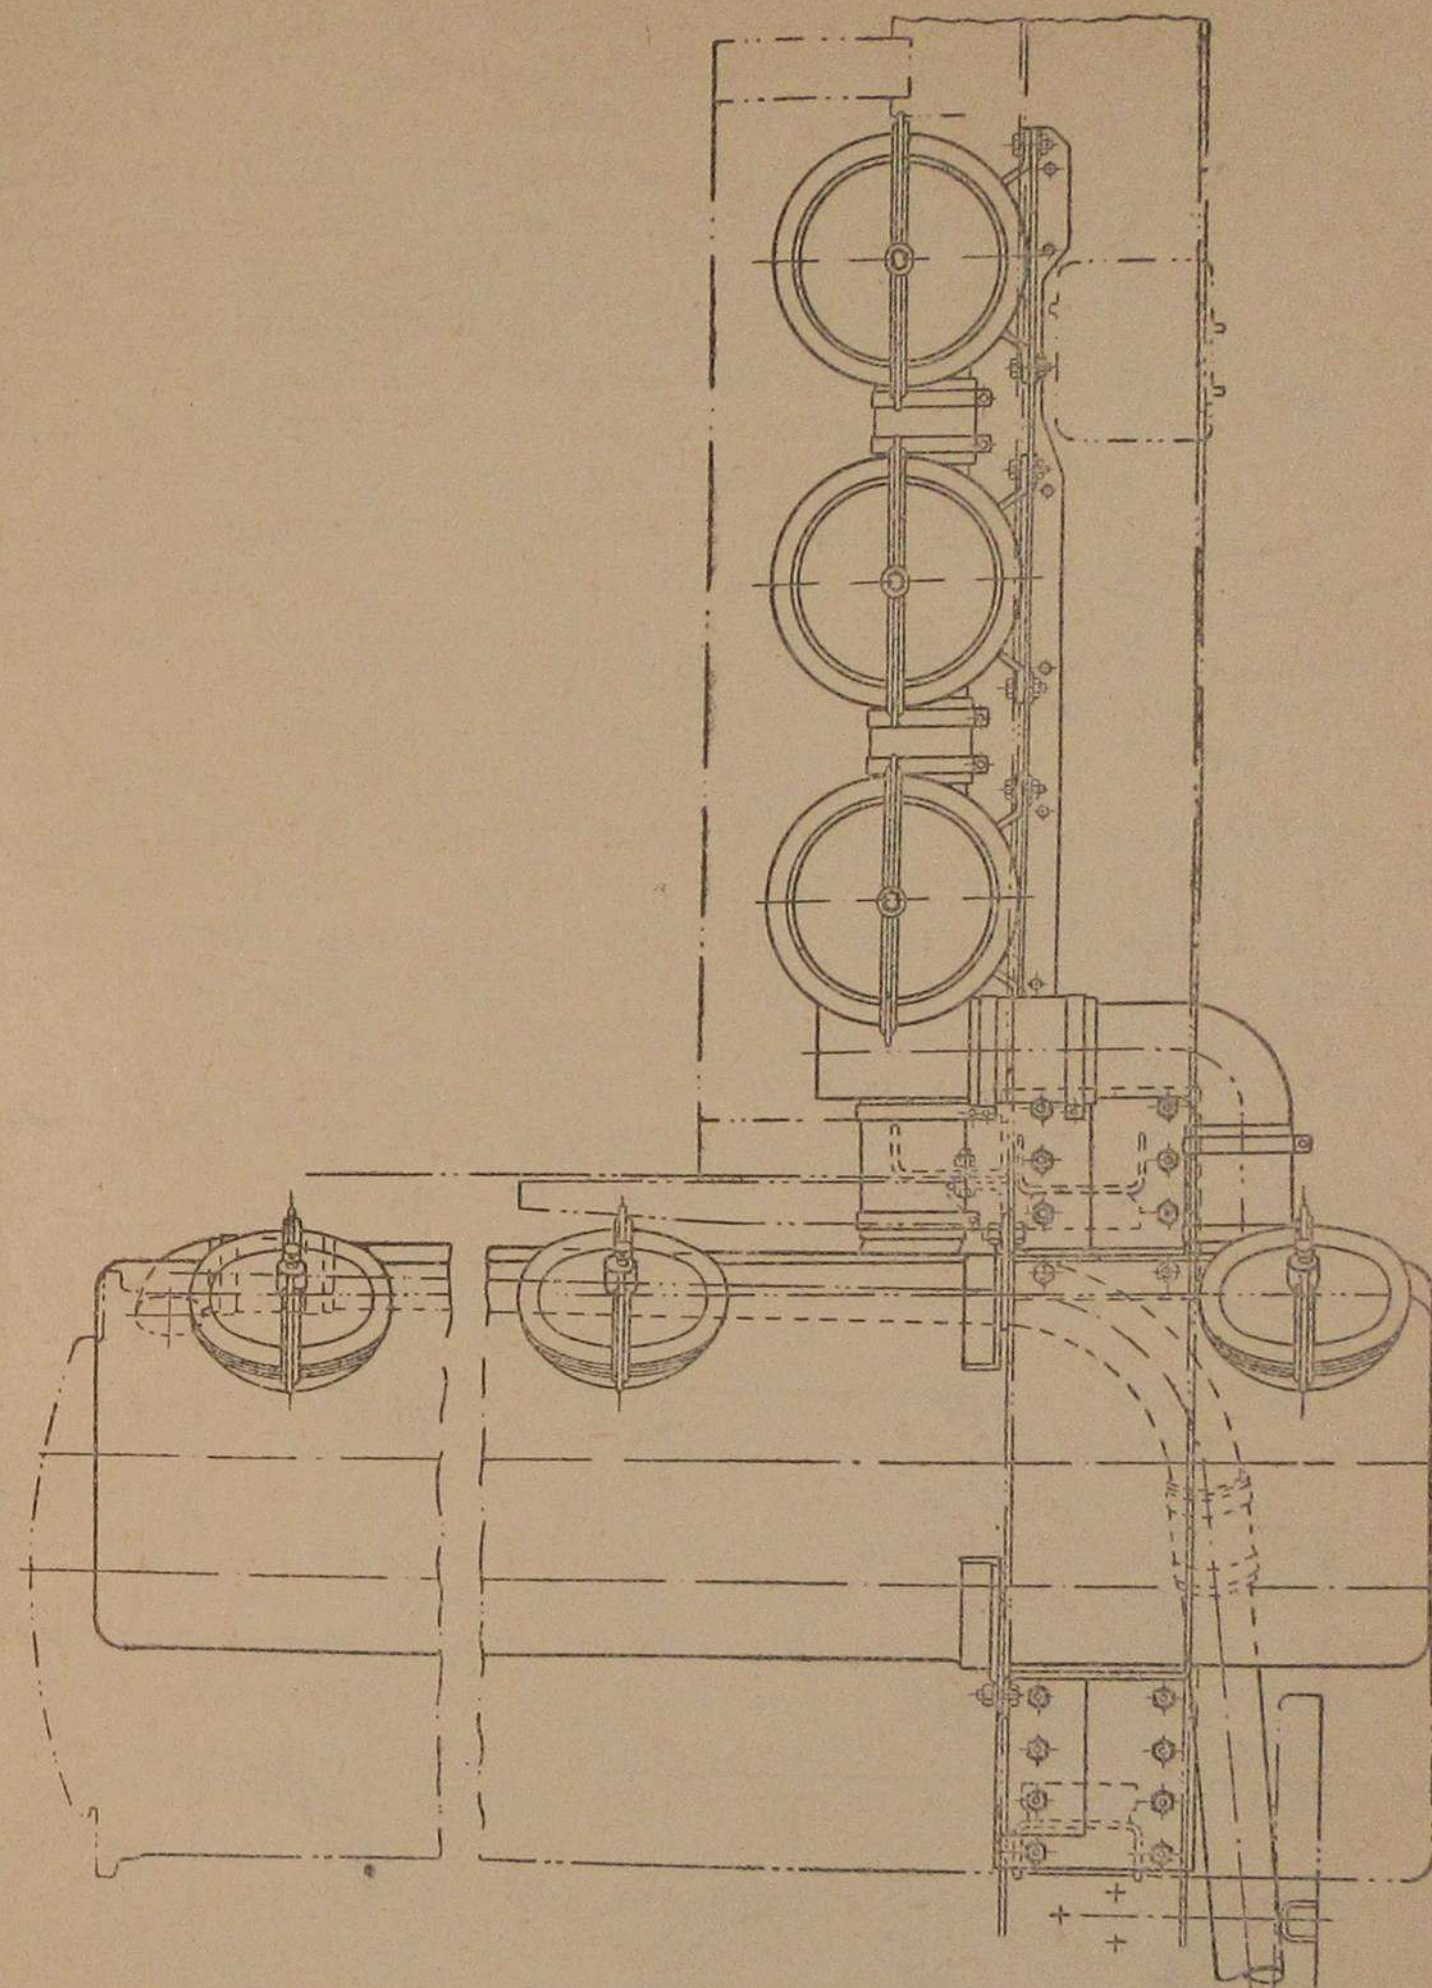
Общий вид сбоку установки и крепления вертикального очистителя ЗИС-21
